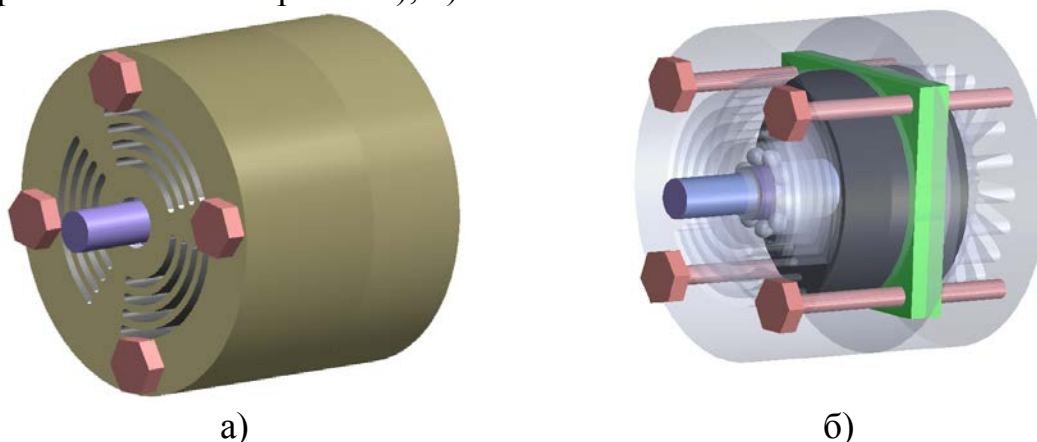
а) общий вид PCB двигателя; б) внутренние узлы и компоненты PCB двигателя в разрезе
